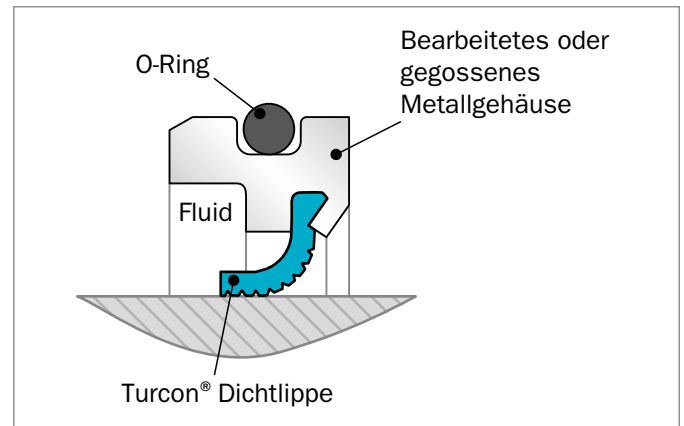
O-Ring-Ausführung; für Passungen mit geringer Interferenz im Einbauraum; Oberflächengüte des Einbauraums > 0,8 µm Ra oder für eine besondere Medienkontrolle
